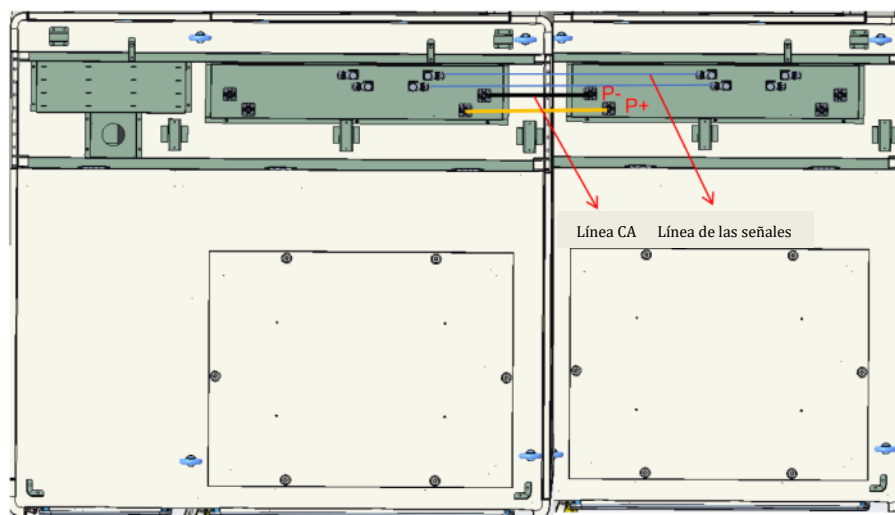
Cableado entre armario de acumulación de energía y armario de la batería
